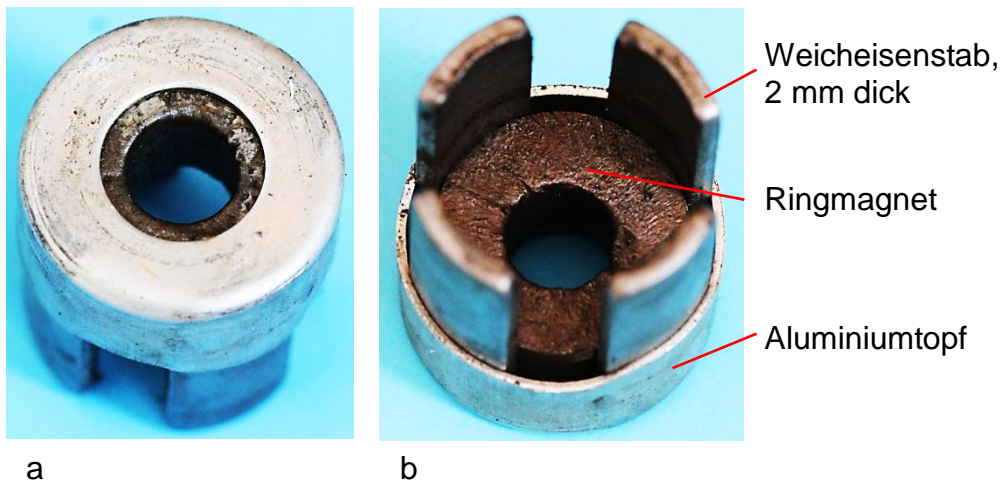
Magnetsystem: a) Aluminiumtopf, b) Radialmagnetisierter Magnetring (Außendurchmesser 23 mm, Innendurchmesser 9 mm, axiale Länge 13 mm)
